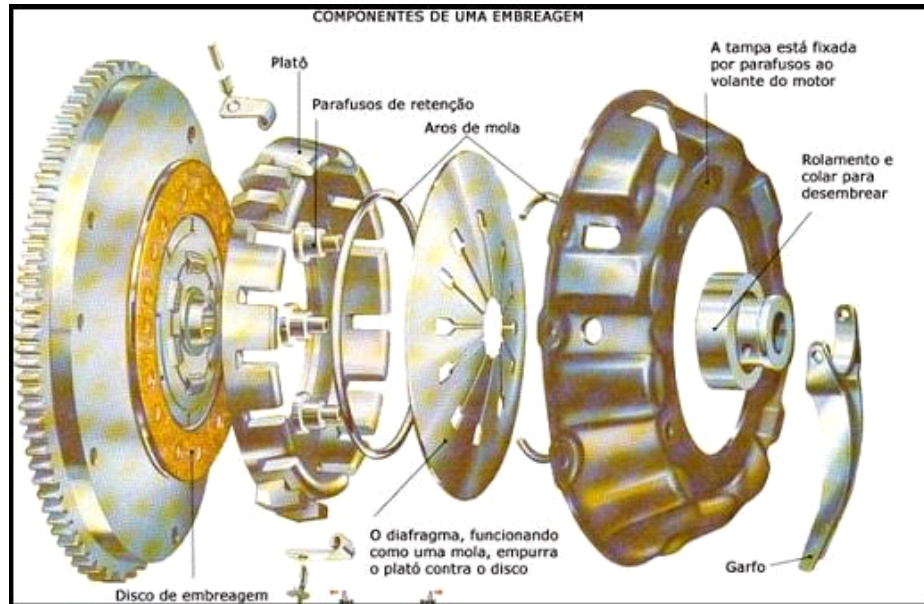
Principais componentes de um conjunto de embreagem automotiva.
